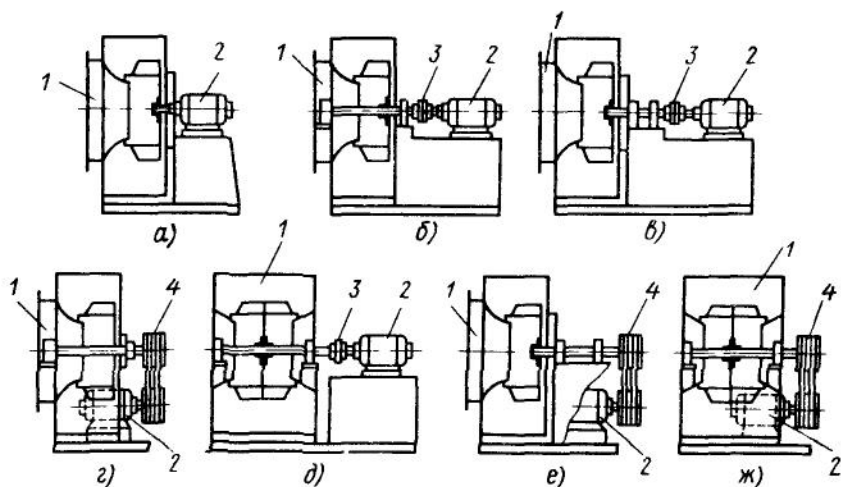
Схемы конструктивных исполнений вентиляторов:
